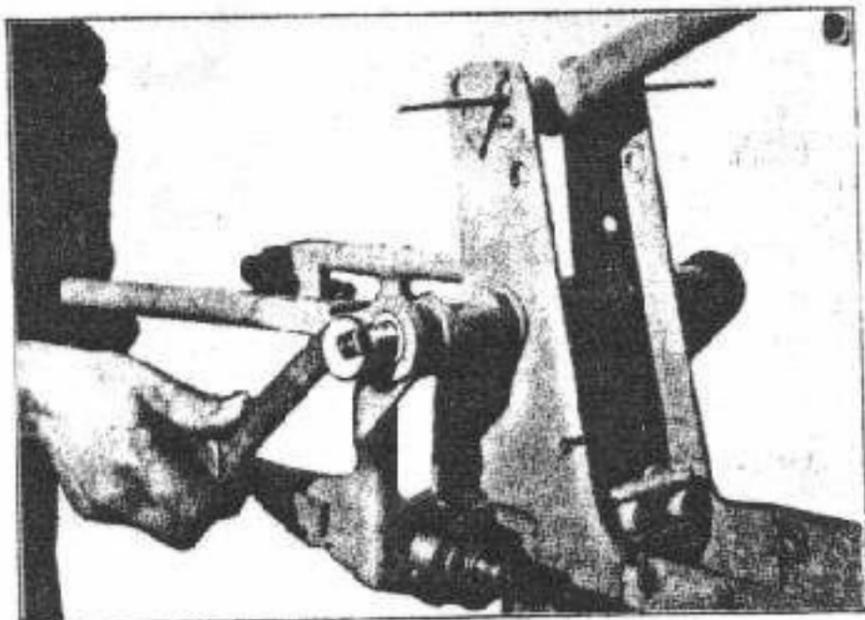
Come si leva il perno principale del forcellone oscillante.
